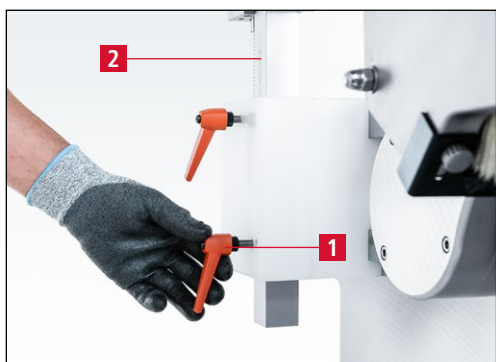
Регулировка ножа в центре шлифовального круга
